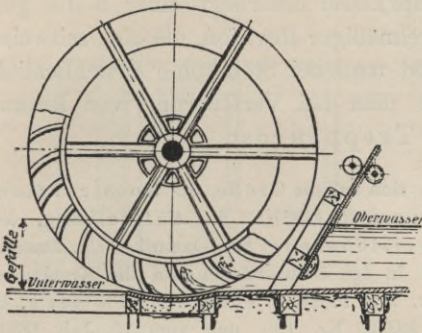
Unterschlächtiges Wasserrad.¹⁾
